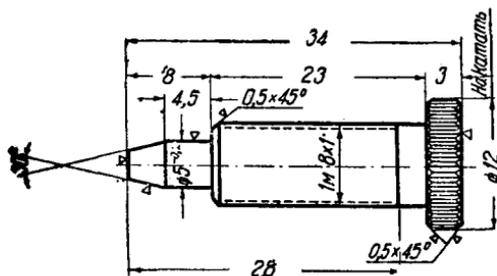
Дет. № 316. Регулирующий винт корпуса дросселя
